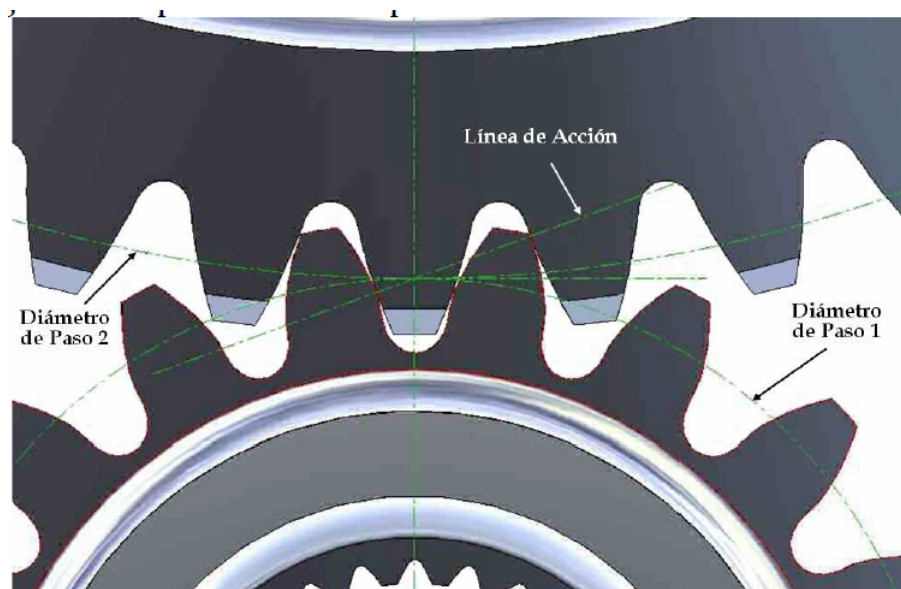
Contacto doble flanco (fuente Gear Co)
